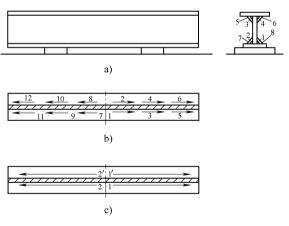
工字梁的焊接顺序 a) 工字梁焊前垫平 b) 单人焊接的焊接顺序 c) 双人焊接的焊接顺序
